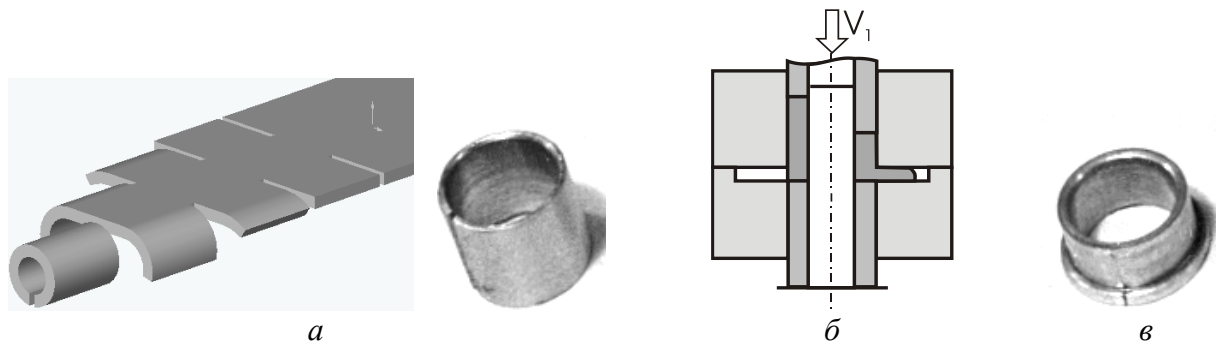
Схеми підготовки заготовки гнуттям (а) і радіального видавлювання (б); деталь після видавлювання (в)
